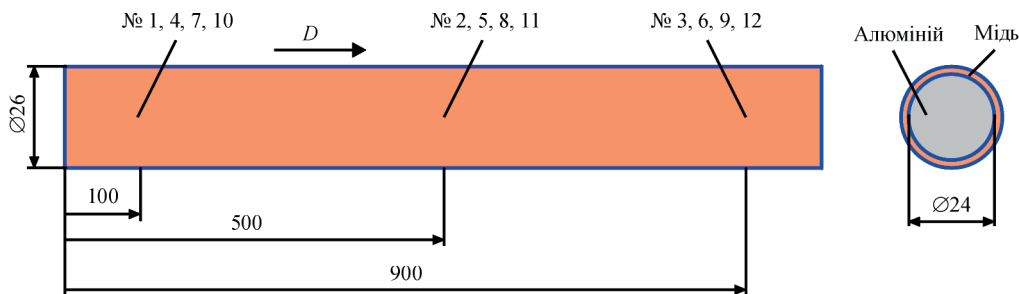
Схема вирізання шліфів з біметалічного стрижня
